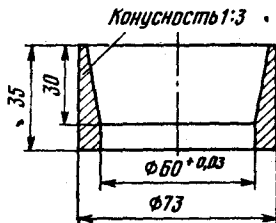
Оправка для установки поршней в цилиндры компрессора
